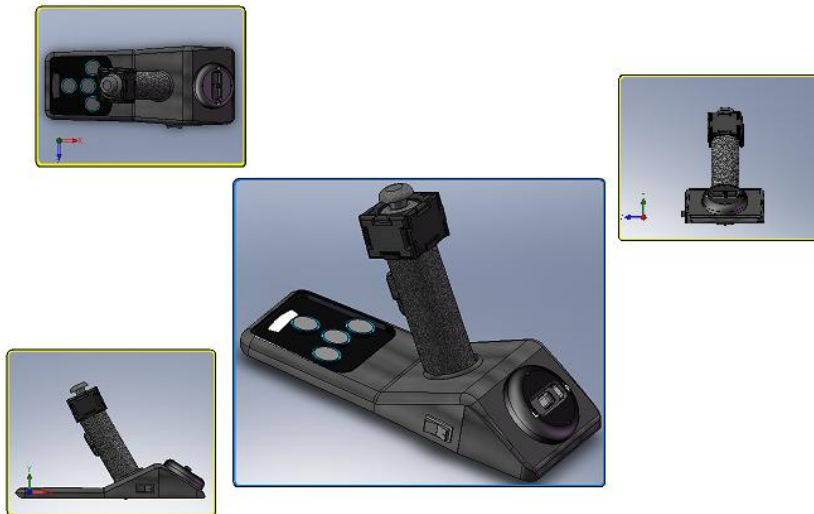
Ensamblaje completo del modulo de control principal en Solidwork
